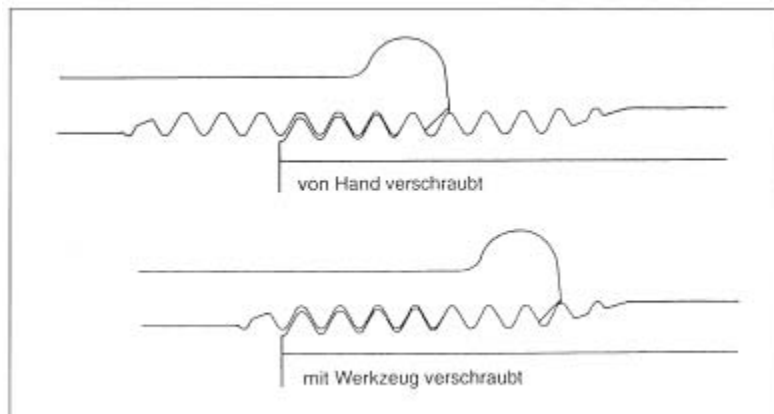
Unverpackte Gewindeverbindung nach EN 10226-1
